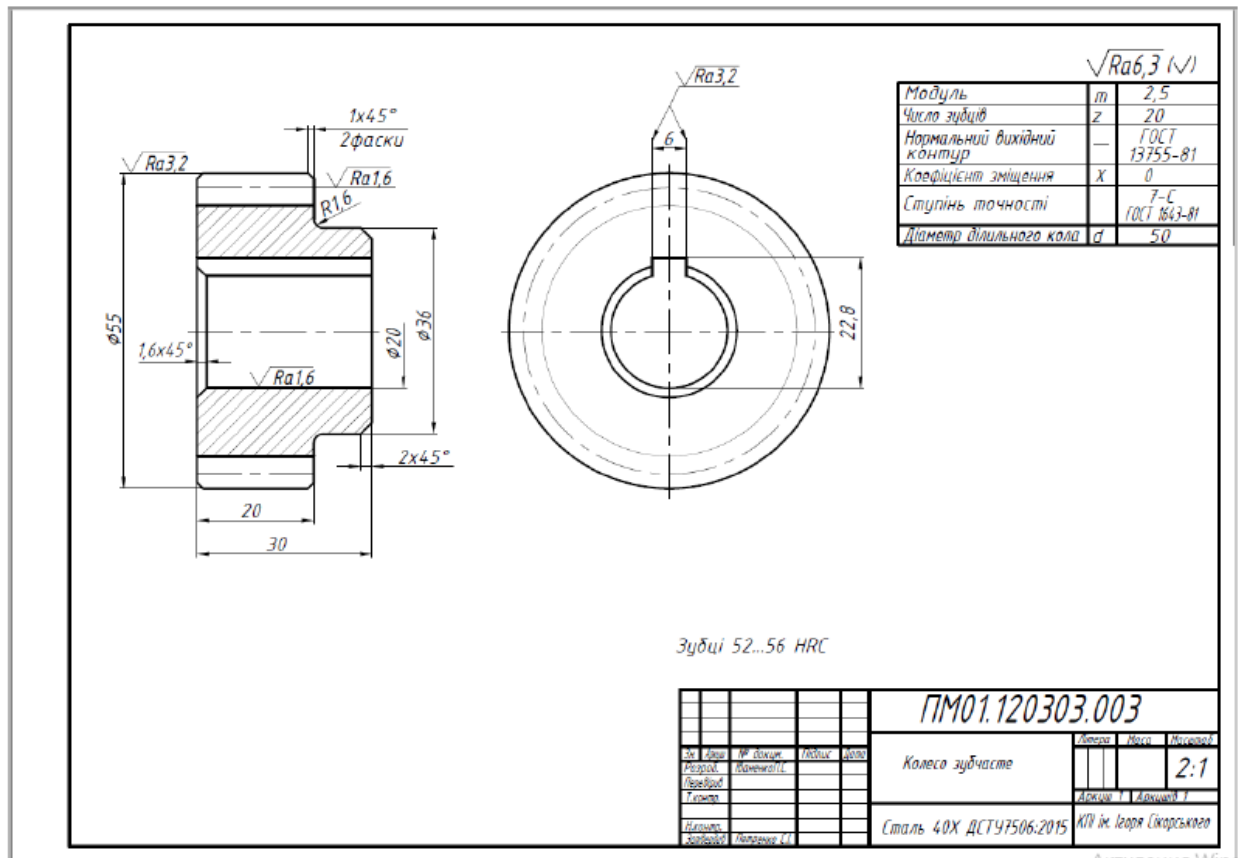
Приклад виконання кресленика «Колесо зубчасте»
